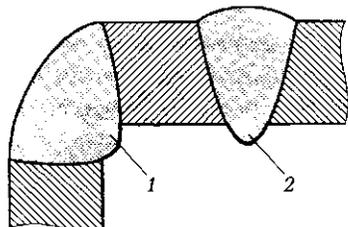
Избыточные выпуклости корня шва углового 1 и стыкового 2 сварных соединений
